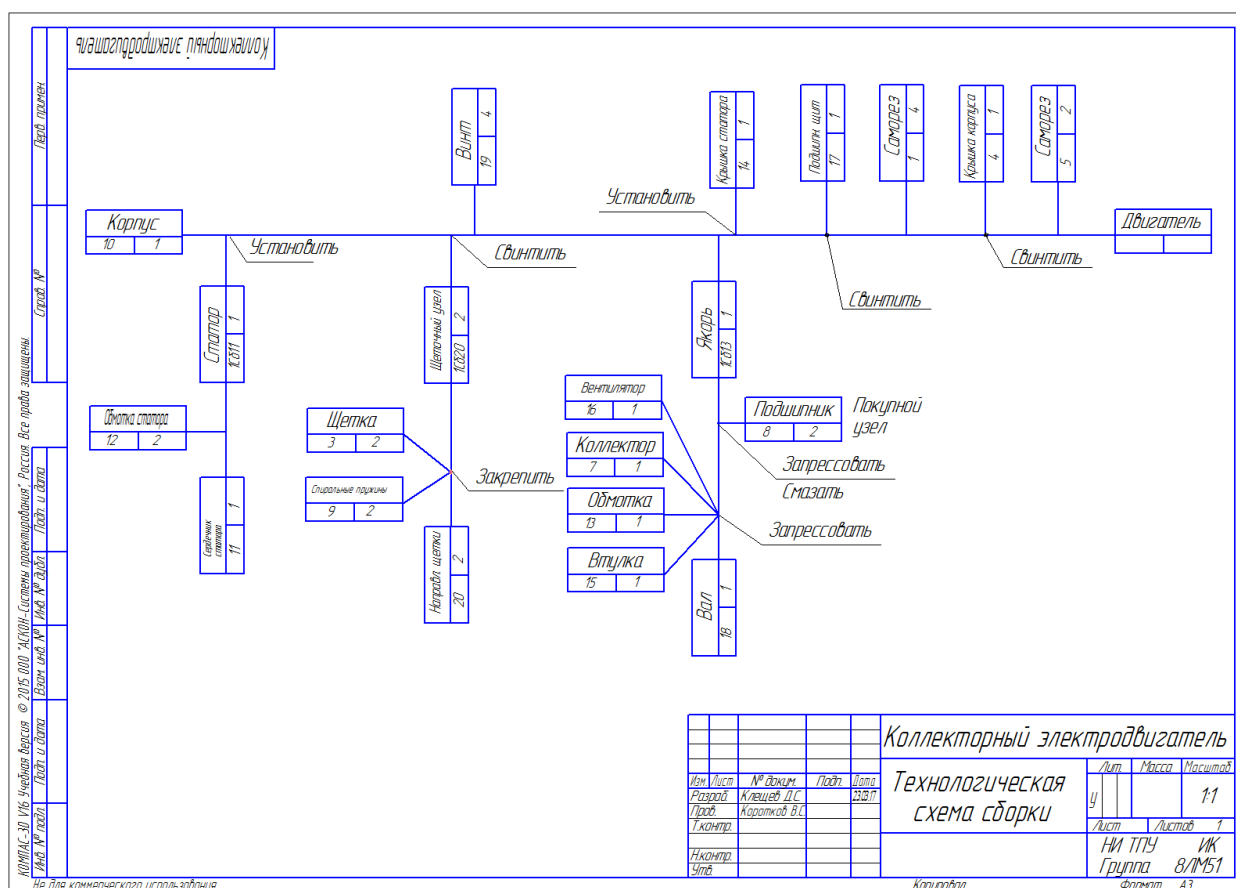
Технологическая схема сборки коллекторного электродвигателя
